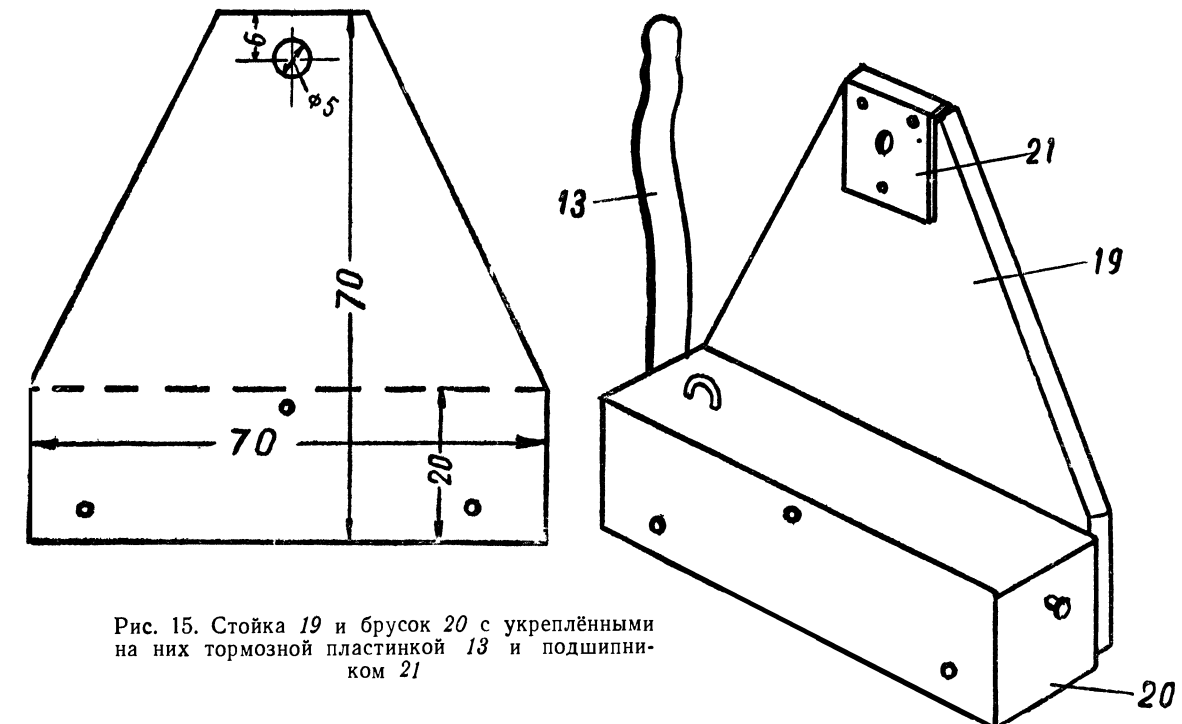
Стойка 19 и брусок 20 с укрепленными на них тормозной пластинкой 13 и подшипником 21
